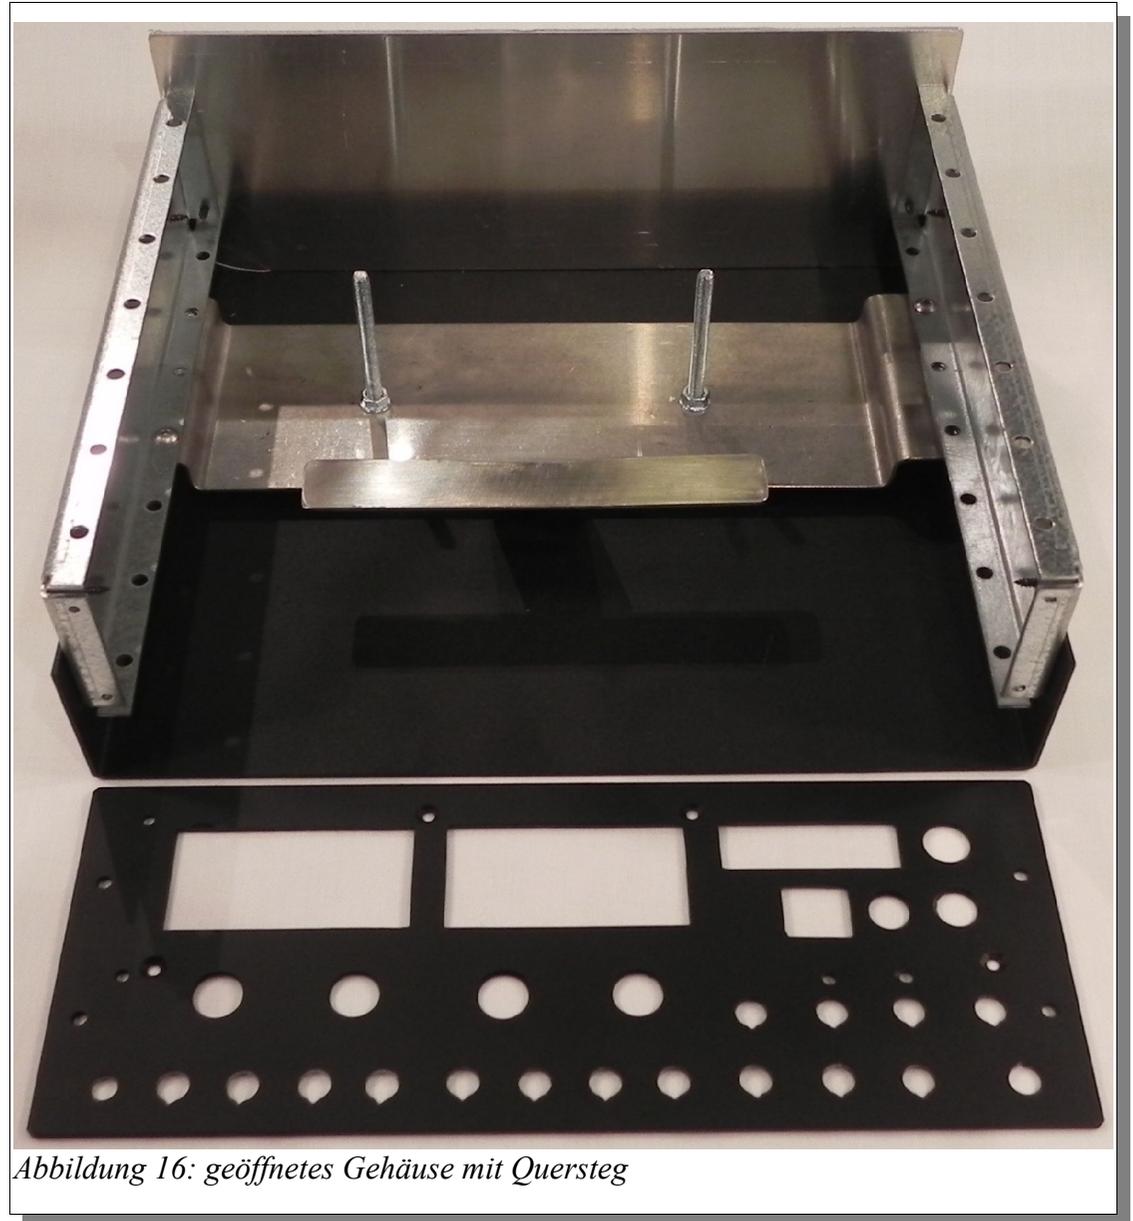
geöffnetes Gehäuse mit Quersteg
